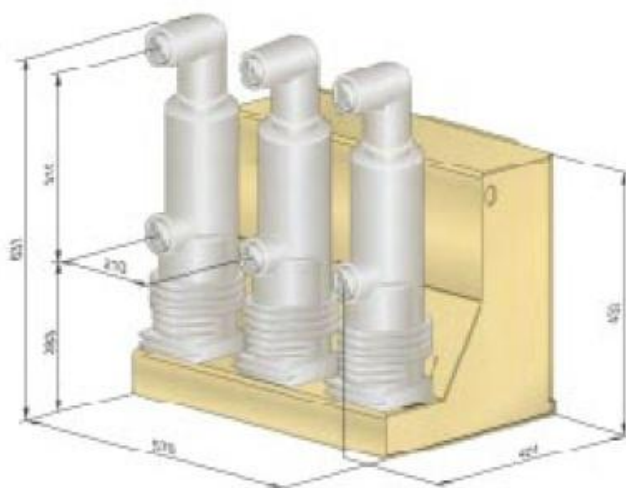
Внешний вид и габаритные размеры выключателя VM1-t 1212-25
